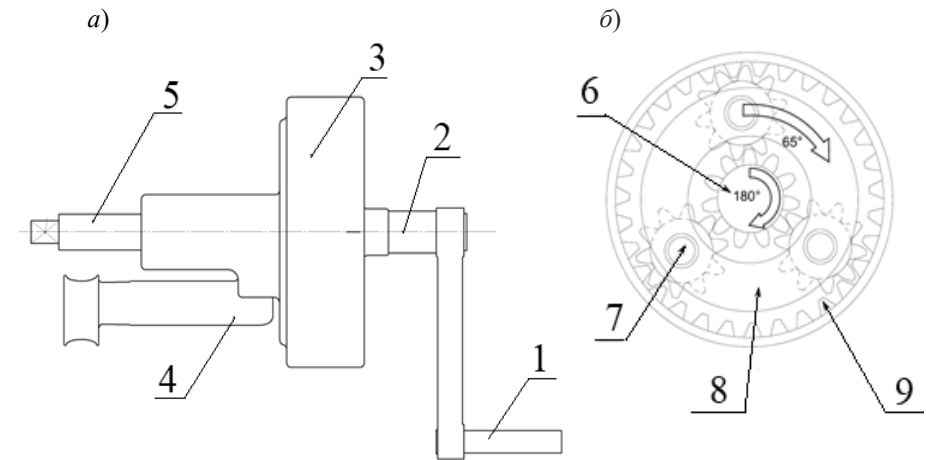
Общий вид (а) и схема планетарного редуктора (б) устройства для отворачивания и заворачивания гаек колес и стремянок рессор
